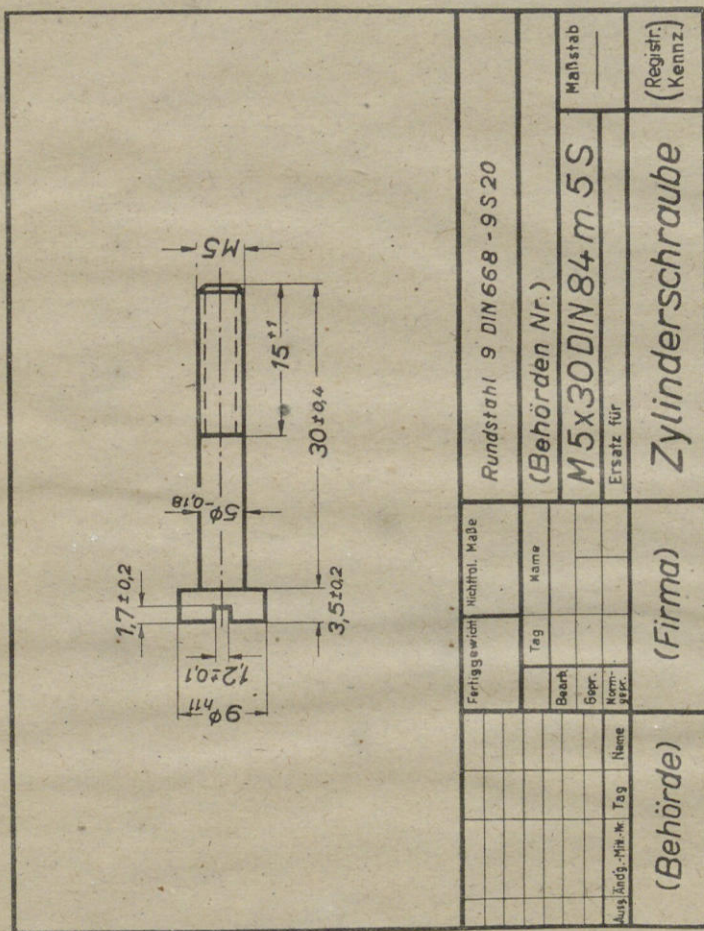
Beispiel einer technischen Zeichnung mit Vordruck: Entwurf DIN 6771
